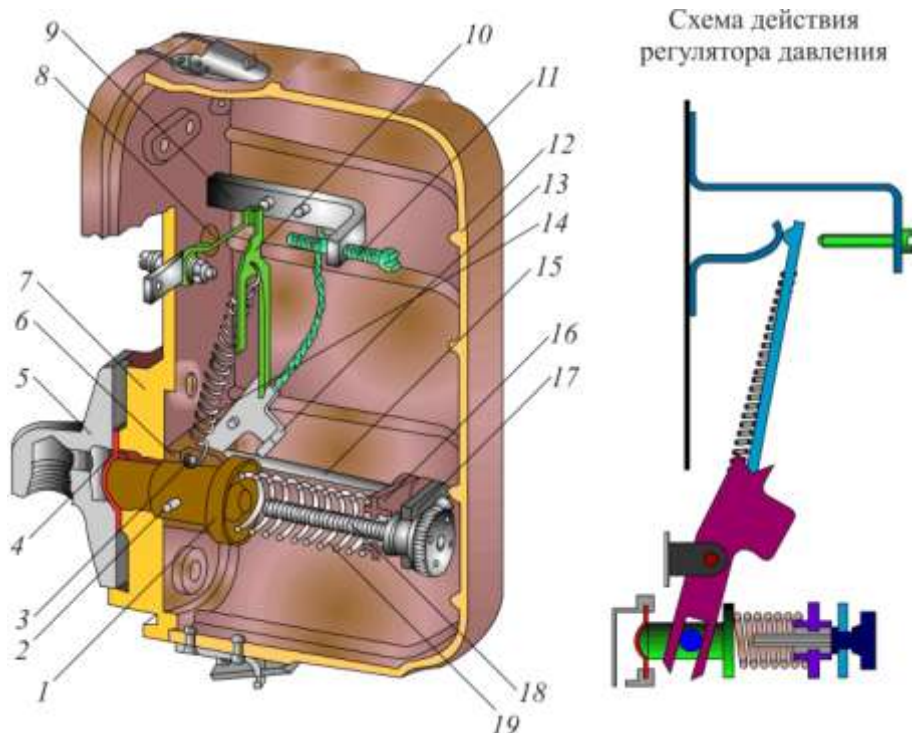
Устройство и схема действия регулятора зарядного давления АК-11Б:
